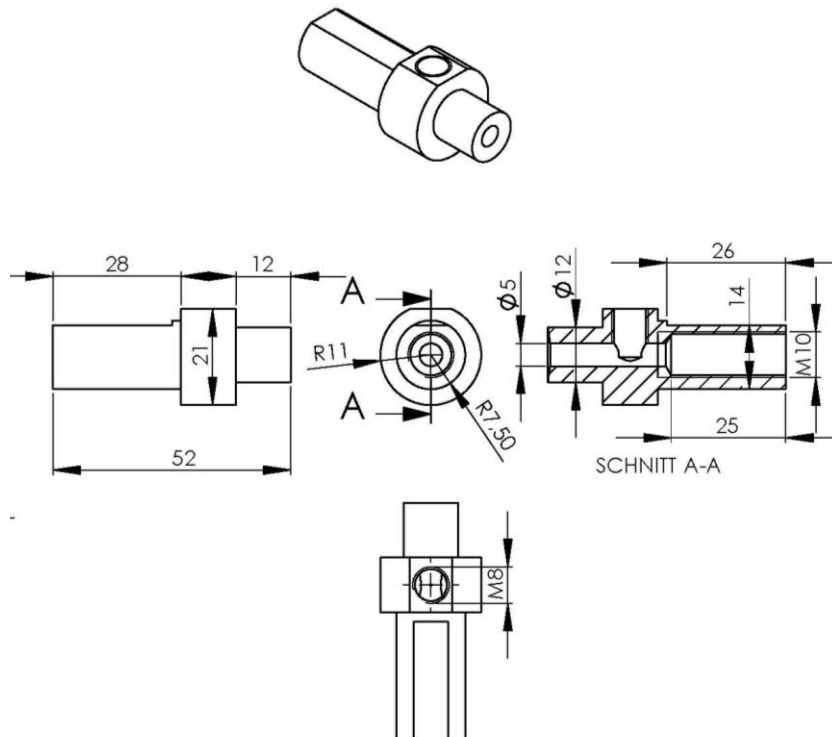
Technische Zeichnung der Werkzeugschulter Werkzeug 2
